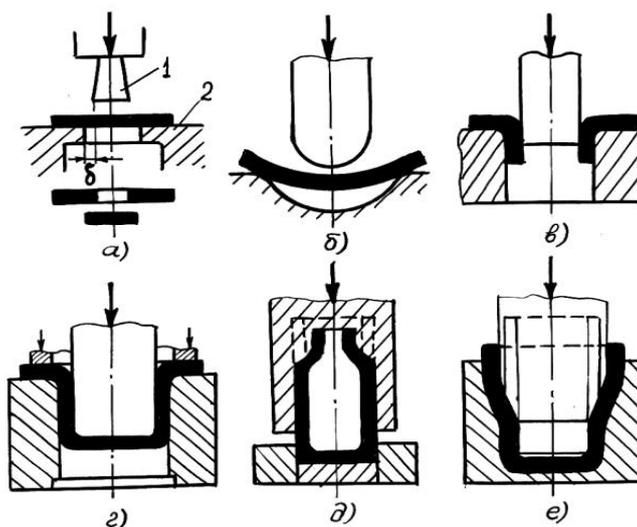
Операции листовой штамповки: а – вырубка и пробивка; б – гибка; в – отбортовка; г – вытяжка;
